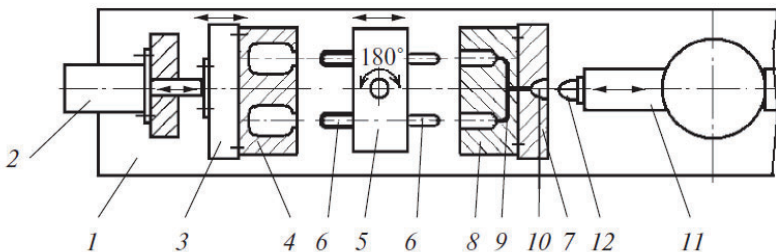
Схема двопозиційного багатомісного інжекційно-роздувного агрегату
